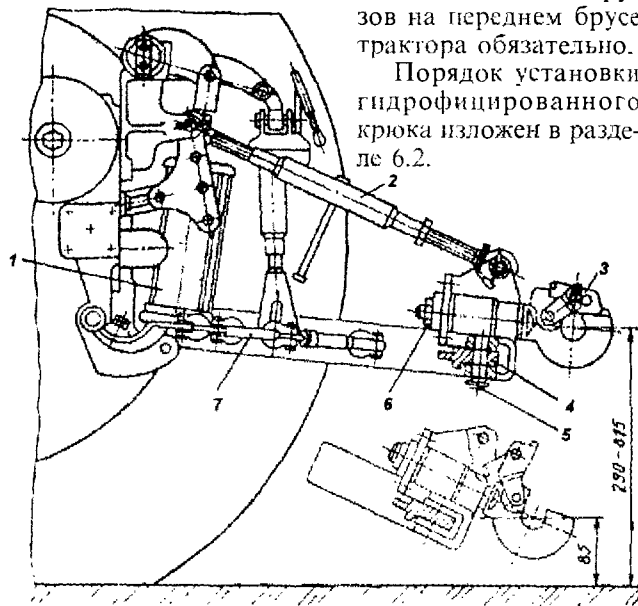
Схема установки тягово-сцепного устройства ТСУ-3-К на тракторах типа ЮМЗ-6КМ: 1 - гидроцилиндр; 2 - центральная тяга; 3 - тягово-сцепное устройство; 4 - поперечина; 5 - палец; 6 - продольная тяга; 7 - стяжка
